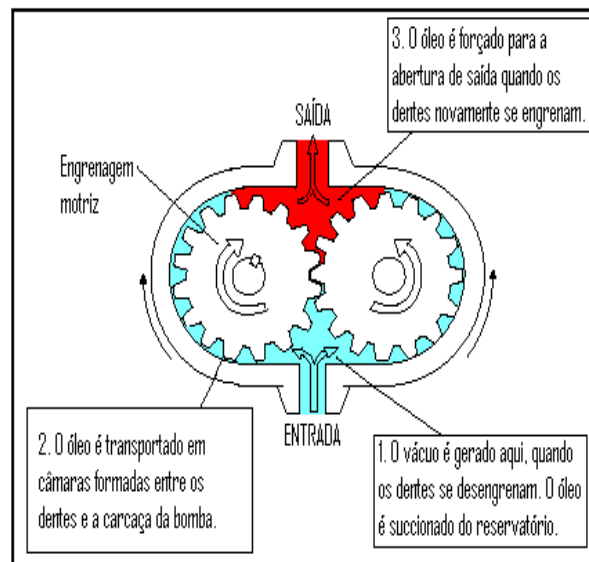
Desenho ilustrativo de bomba de engrenagens.
